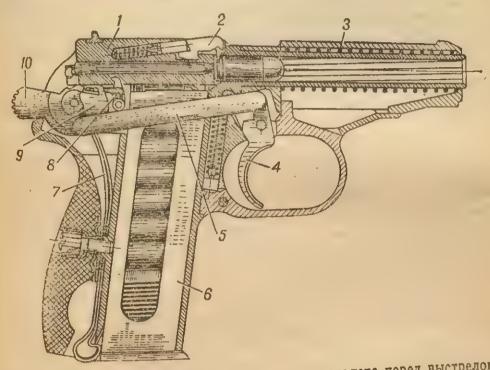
Положение частей и механизмов пистолета перед выстрелом: 1— затвор; 2— выбрасыватель; 3— возвратная пружина; 4— спусковой крючок; 5— спусковая тяга; 6— магазин; 7— боевая пружина; 8— шептало спужиной; 9— рычаг взвода; 10— курок
